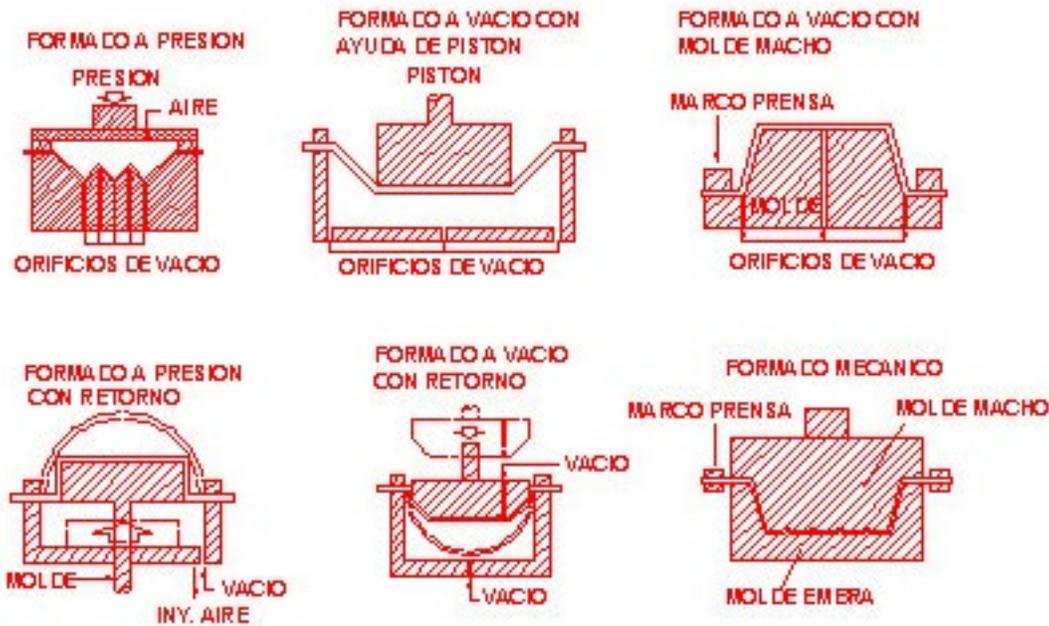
Técnicas de Formado para la Lámina Acrílica
